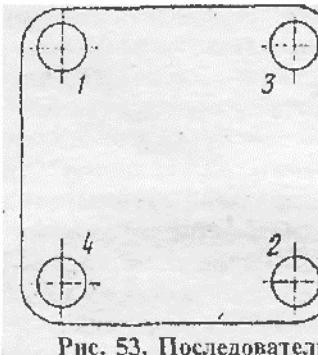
Последовательность затяжки гаек крепления головок цилиндров
